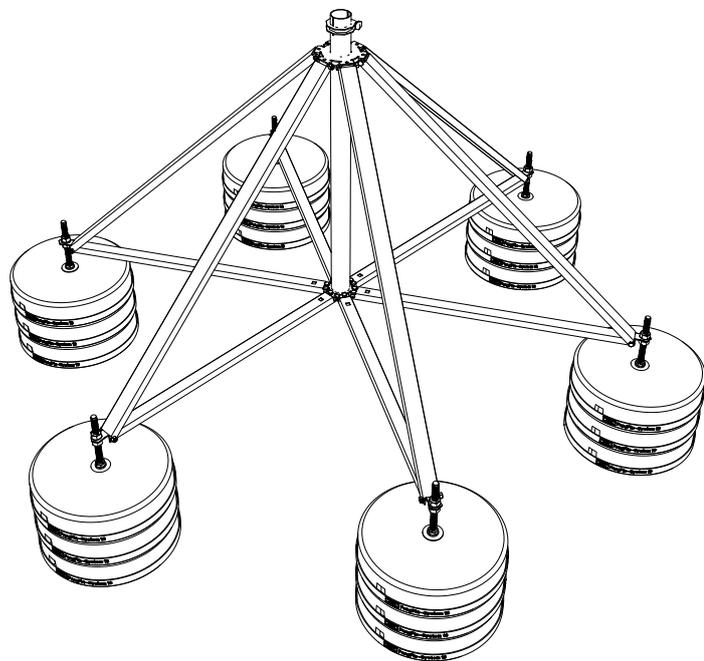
Erhöhung des Gewichts und Stabilisierung mit Betonsteinen
